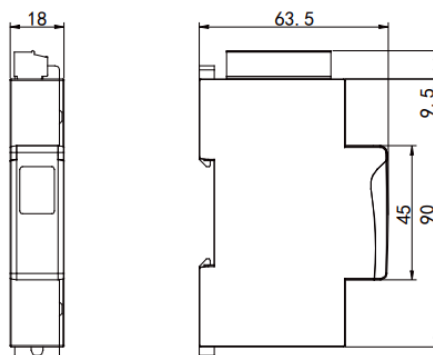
Внешний вид и габаритные размеры модуля связи C14
